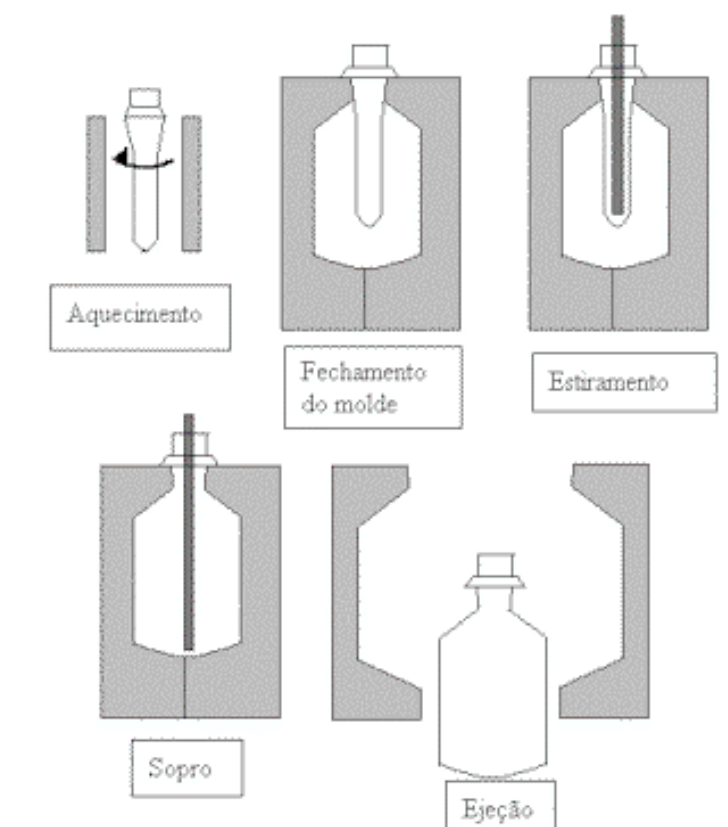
Ilustração do processo de moldagem por sopro via injeção
